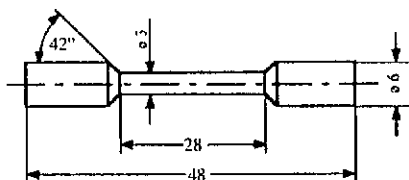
Dessin des éprouvettes de fluage. Les dimensions sont données en mm.
